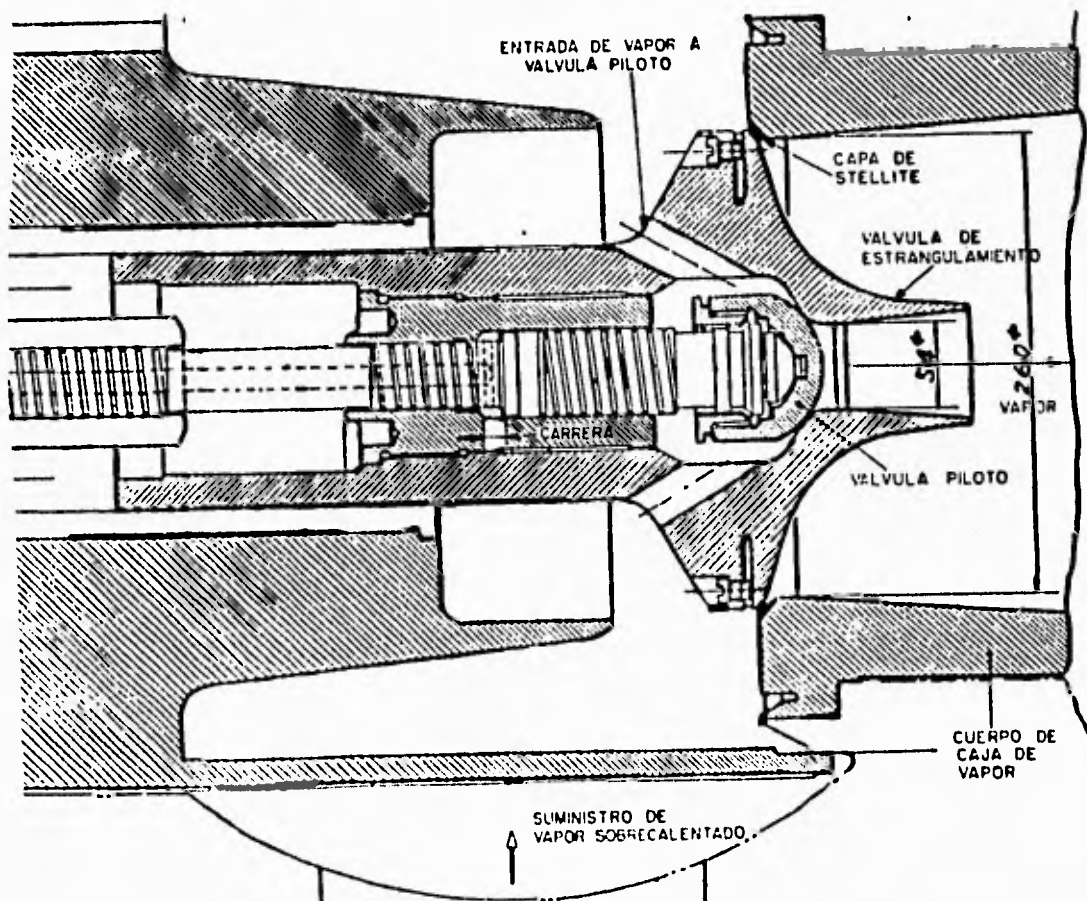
DETALLE DE VALVULAS DE ESTRANGULAMIENTO Y PILOTO
